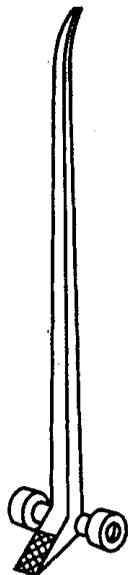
Тележки для перевозки грузов и монтажных заготовок:
